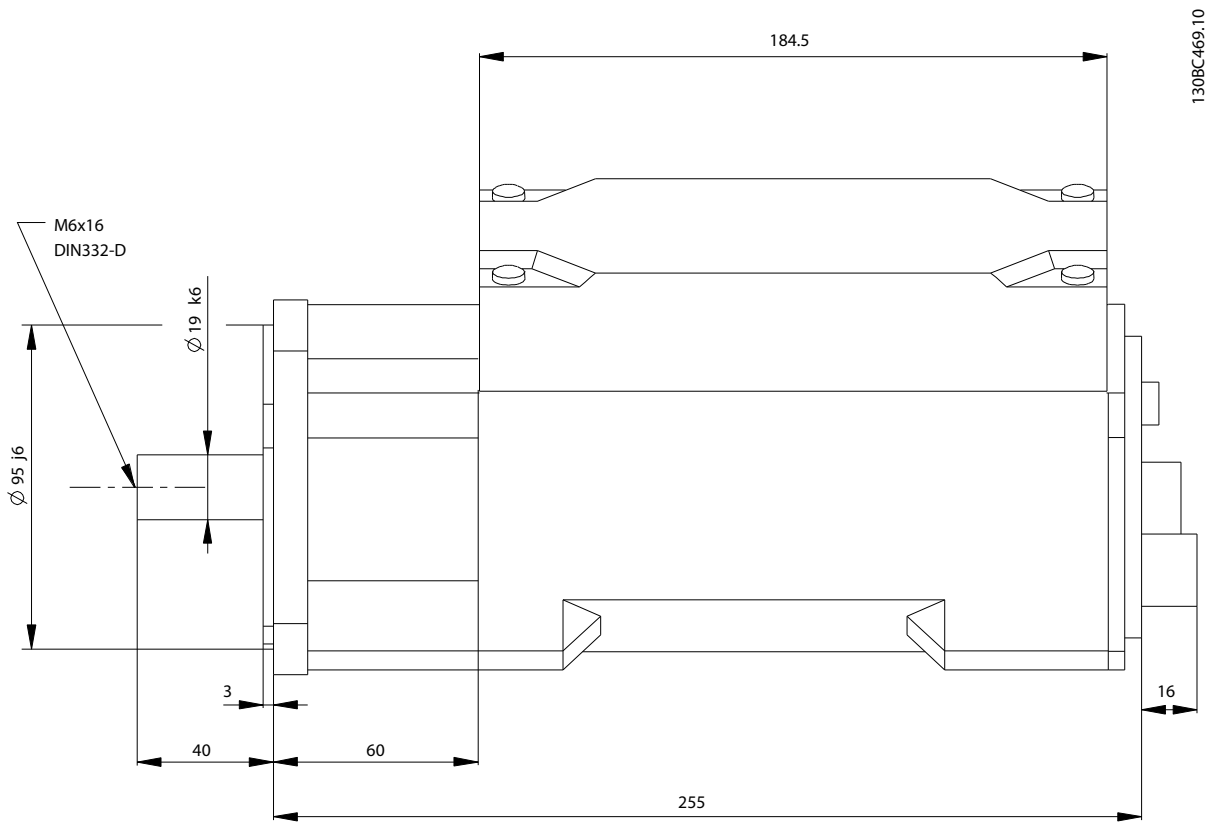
Seitenansicht: Servomotor mit IEC Flansch und Bremse
